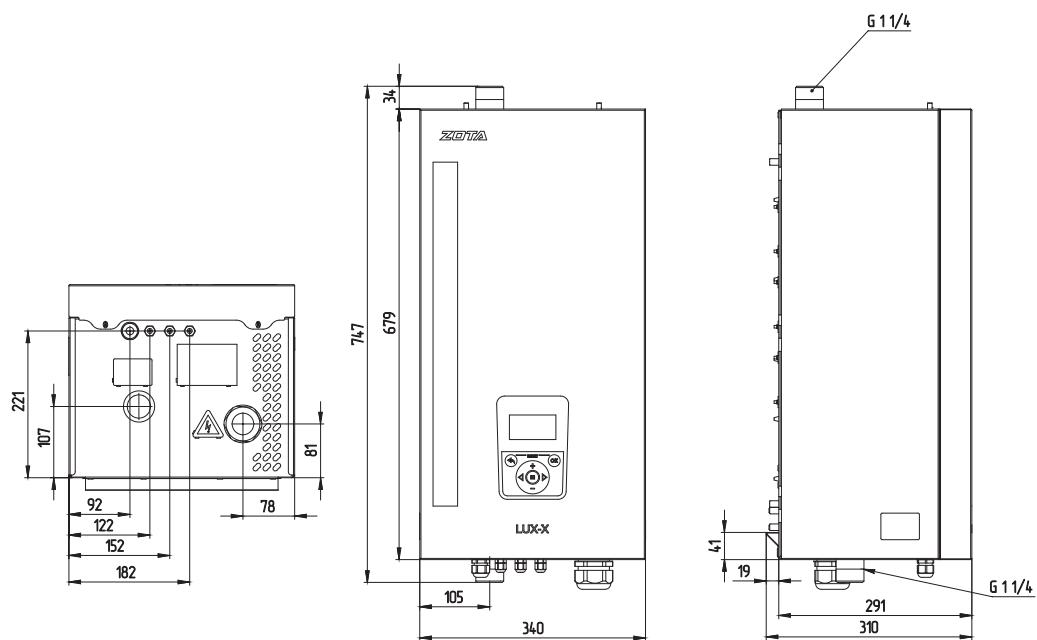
Габаритные размеры ZOTA LUX-X 30-36
